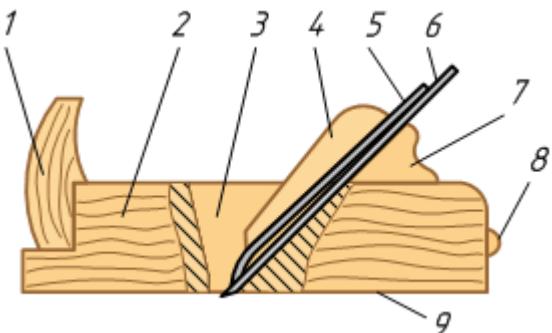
Устройство деревянного рубанка с двойным ножом
